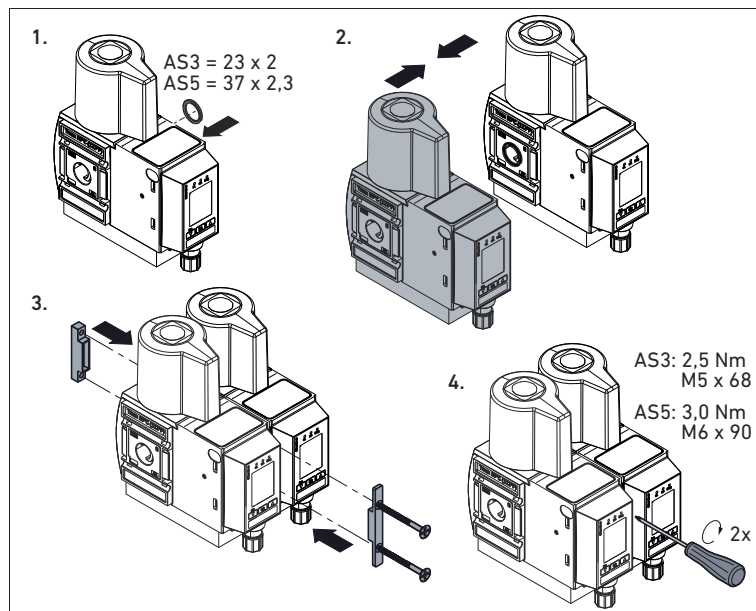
Fissaggio dell'elemento di collegamento nelle valvole in batteria
